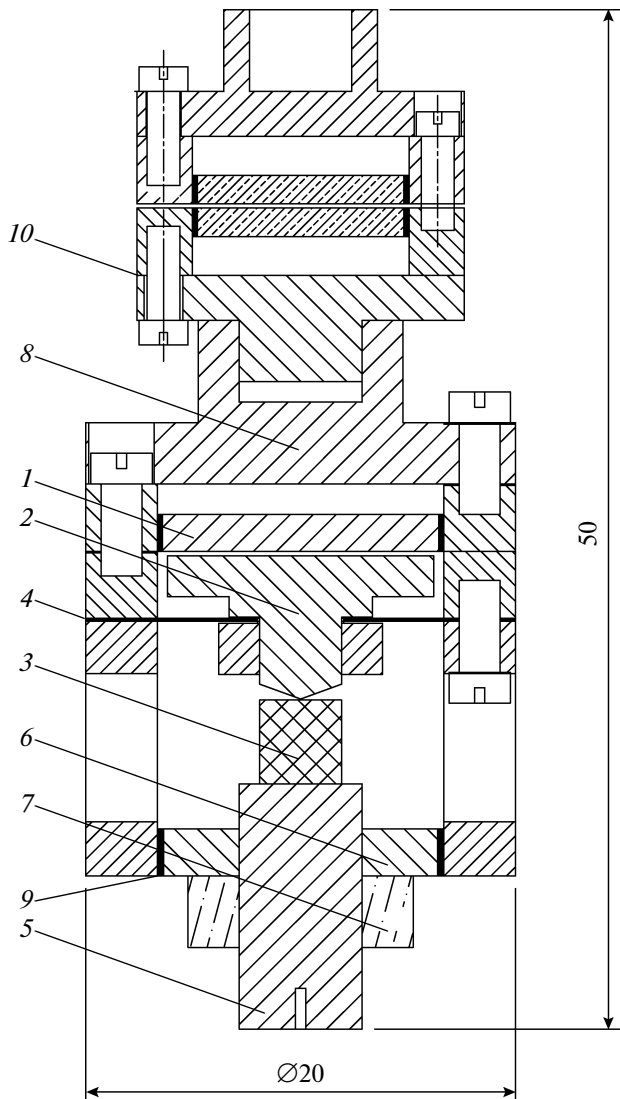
Схема емкостного датчика dilatометра. 1 – неподвижная пластина плоского конденсатора; 2 – подвижная пластина конденсатора; 3 – образец; 4 – кольцевая мембрана (пружина); 5 – винт с опорной поверхностью для размещения образца; 6 – нижняя пластина датчика; 7 – контргайка; 8 – верхняя крышка датчика; 9 – эпоксидная смола Stycast; 10 – опорный конденсатор, предназначенный для нормирования измерений, выполненных под давлением.
